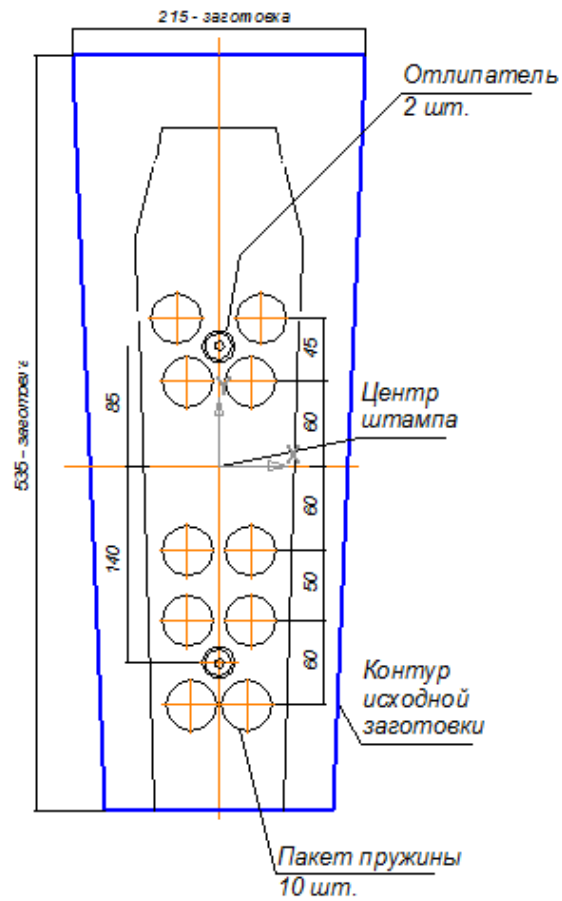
Пакеты пружин и отлипатели в верхней части вытяжного штампа
